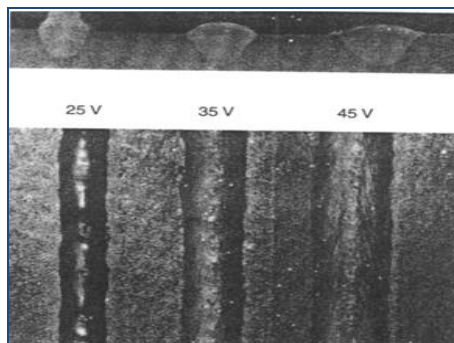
Efecto del voltaje en el proceso de soldadura (SAW) [15].
